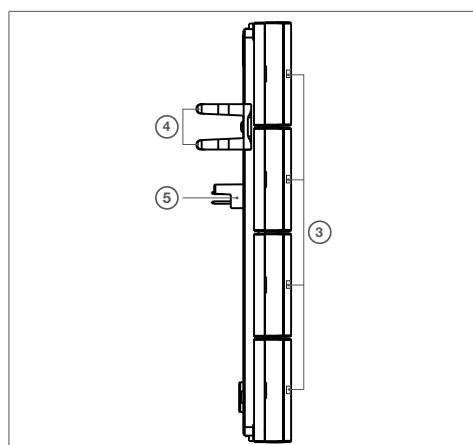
Vue de profil du bloc bouton poussoir 8 touches
